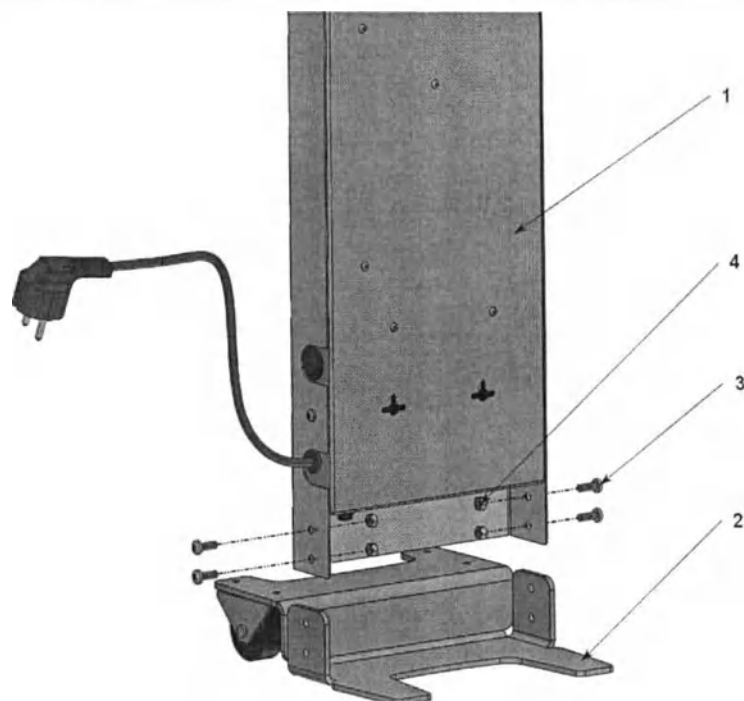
Монтаж облучателя на мобильную опору. 1- Облучатель; 2- Опорная стойка; 3- Винт М5; 4- Гайка М5.
